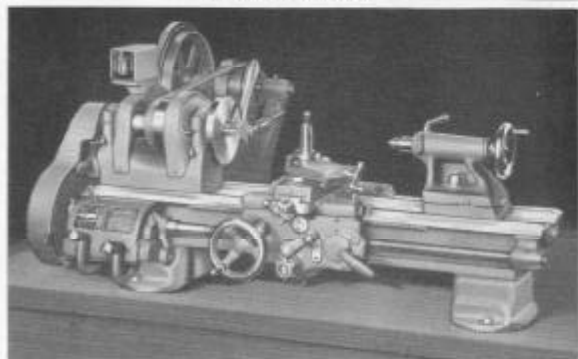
Un torno de banco modelo "A" con voltes de 225 mm con transmisión horizontal ajustable de motor
